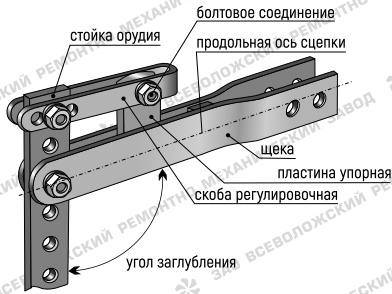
Установка сцепки опорной пластиной вверх (стандартно).
